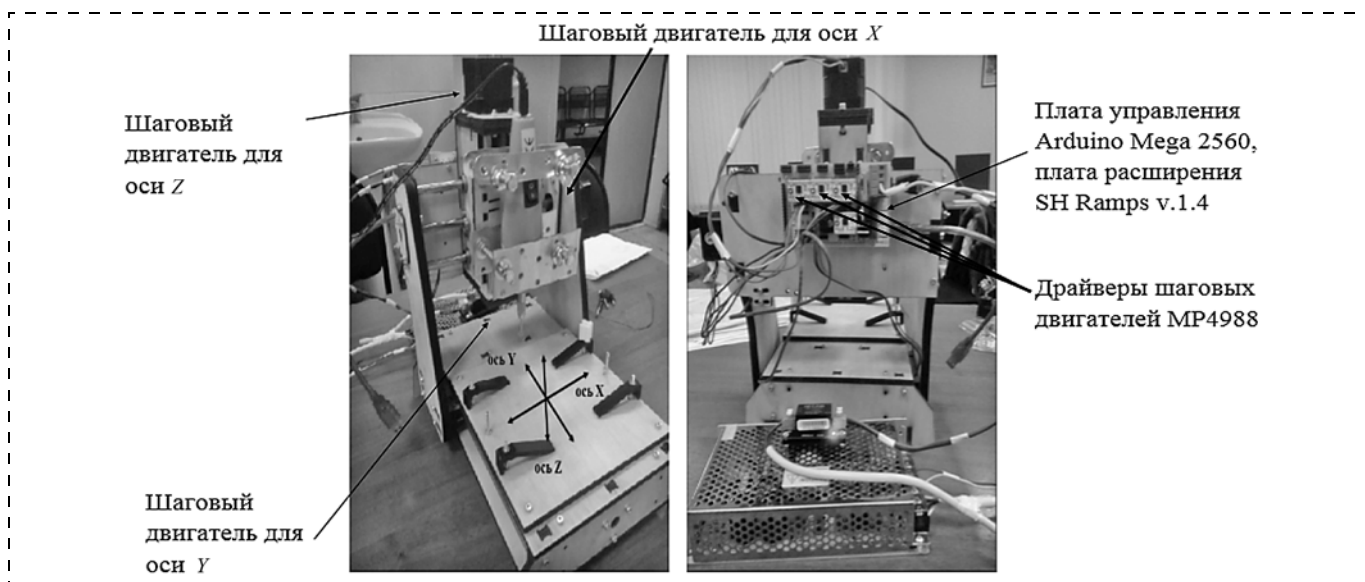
Трехосевой фрезерный станок с ЧПУ
